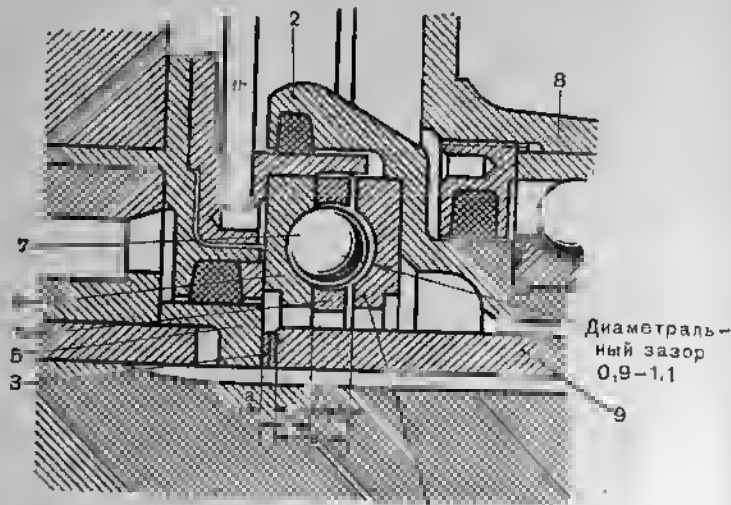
Определение толщины регулировочных прокладок: 1 — кольцо выключателя подвижной чашки; 2 — подвижная чашка; 3 — регулировочные прокладки; 4 — сепаратор; 5 — проставочное кольцо; 6 — кольцо выключателя неподвижной чашки; 7 — шарик; 8 — отжимной диск; 9 — ведущий барабан
